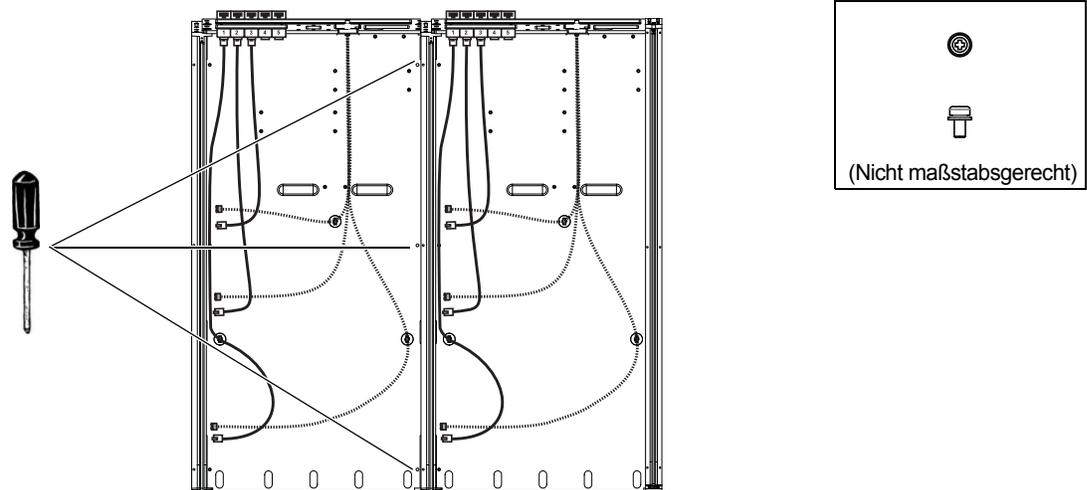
Befestigen der Bodenplatte des ersten Chassis an der Seitenwand des zweiten Chassis
